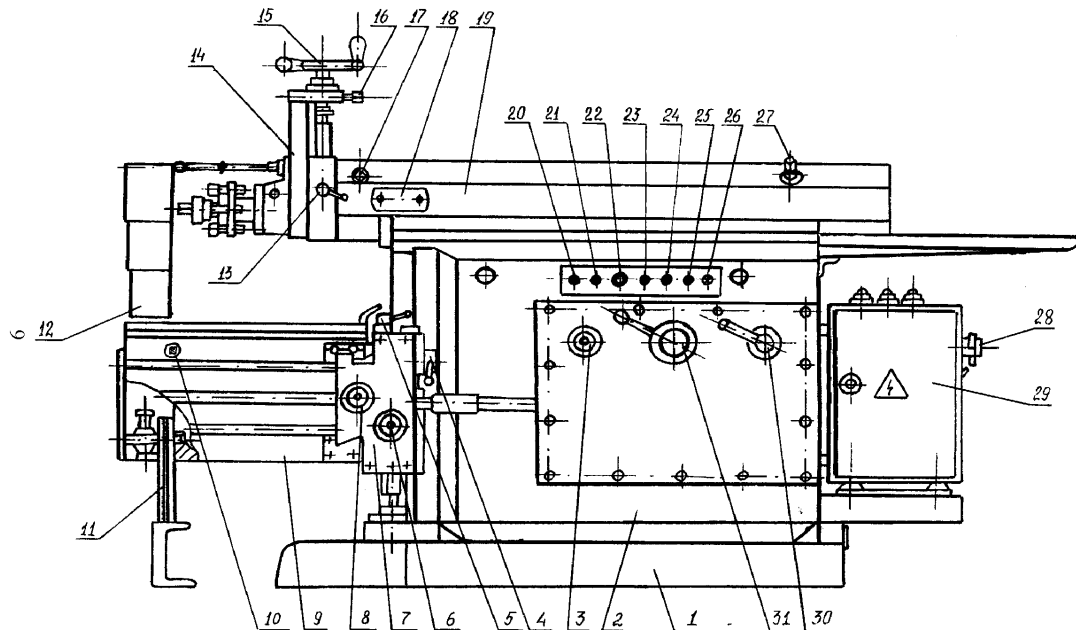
Поперечно-строгальный станок модели 7307ГТ (вид сбоку):
